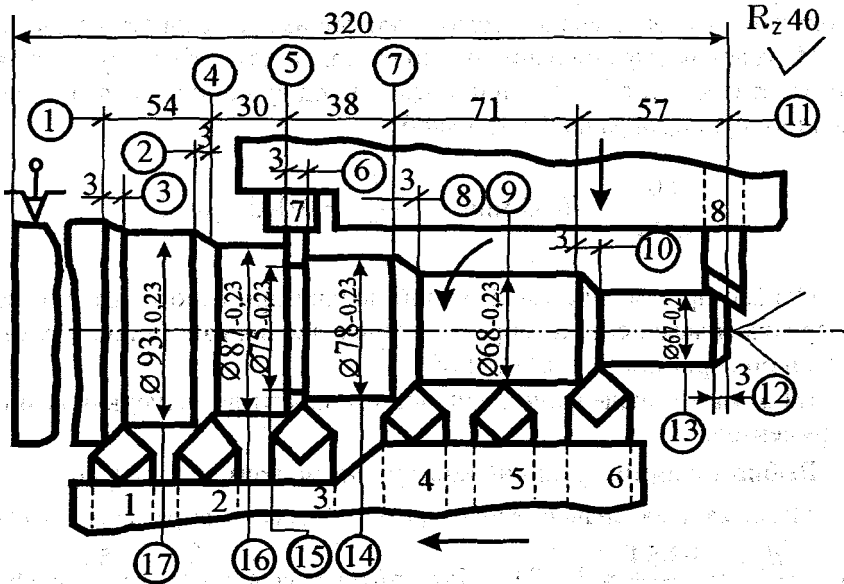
Эскиз обработки кожуха полуоси
